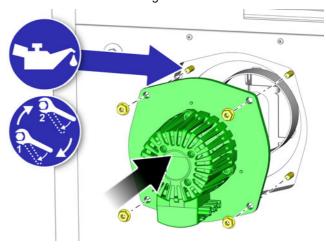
Nettoyage du rotor et remplacement du joint
